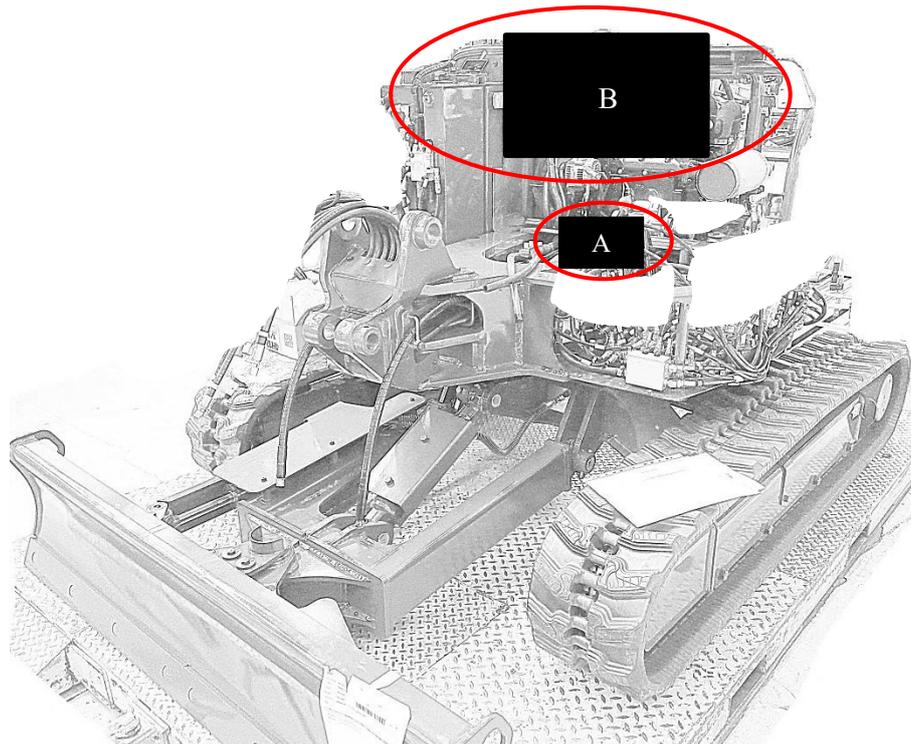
montaggio motore di rotazione (A) e supporto posto guida posteriore (B)
